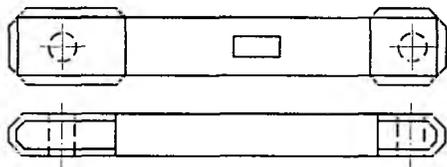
Калибры для контроля деталей шлицевых соединений:
